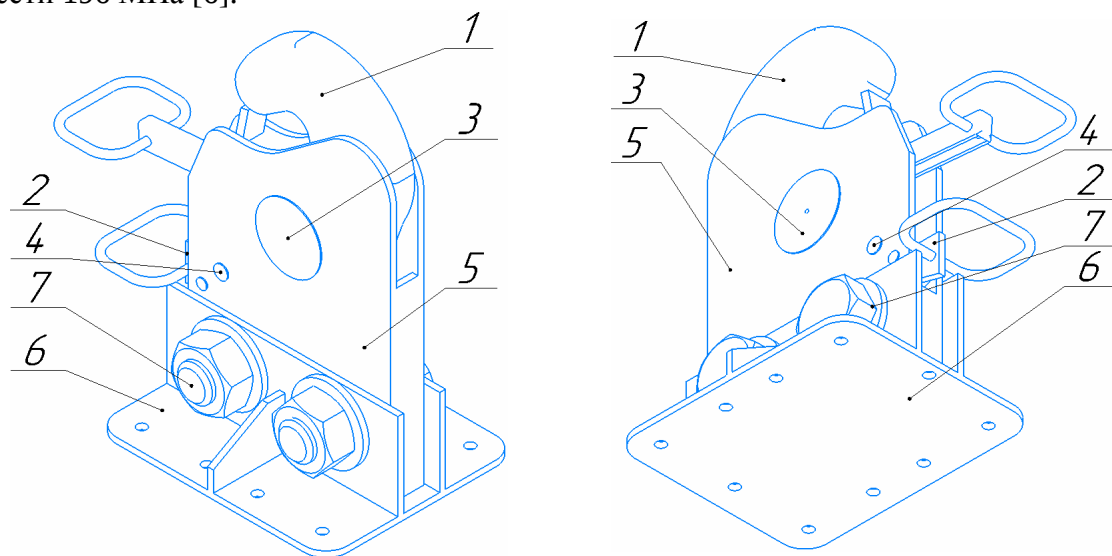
Общий вид гака: 1 – крюк, 2 – фиксатор, 3 – палец крюка, 4 – упор фиксатора, 5 – корпус гака, 6 – фланец крепления к катеру, 7 – болт М48
